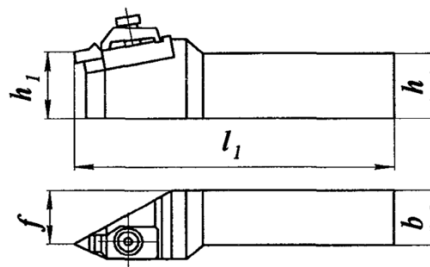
Різьбовий різець з механічним кріпленням ромбічних пластин для нарізування метричної різьби
